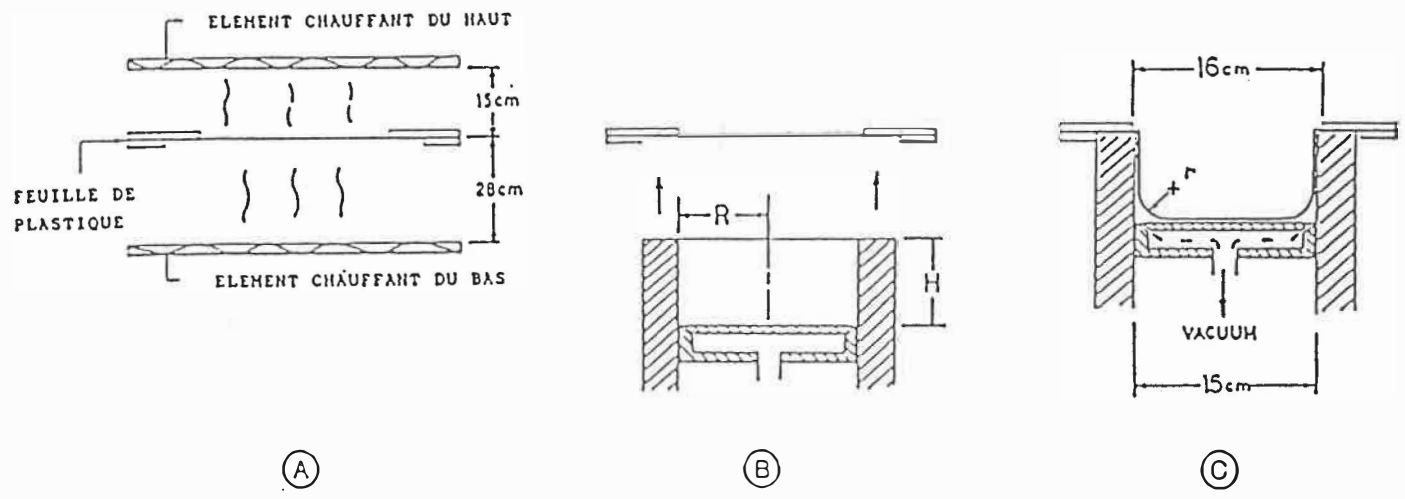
Schématique de la machine de thermoformage et du moule.
